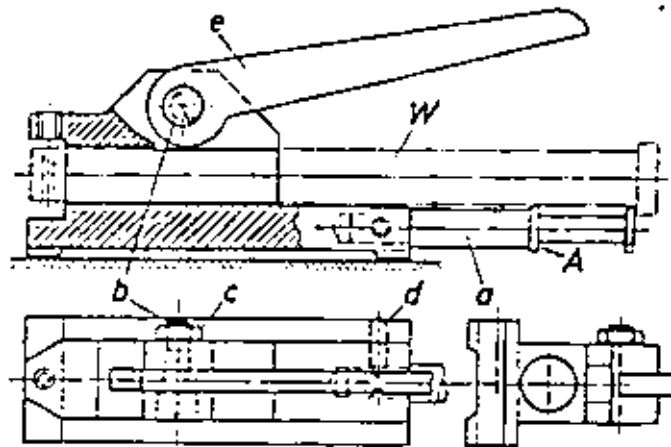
Utilaje para taladrar con excéntrica de fijación de arco plano
